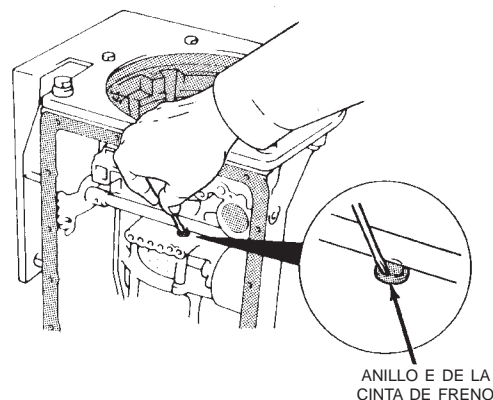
Desmontaje del conjunto de embrague directo y de marcha adelante
